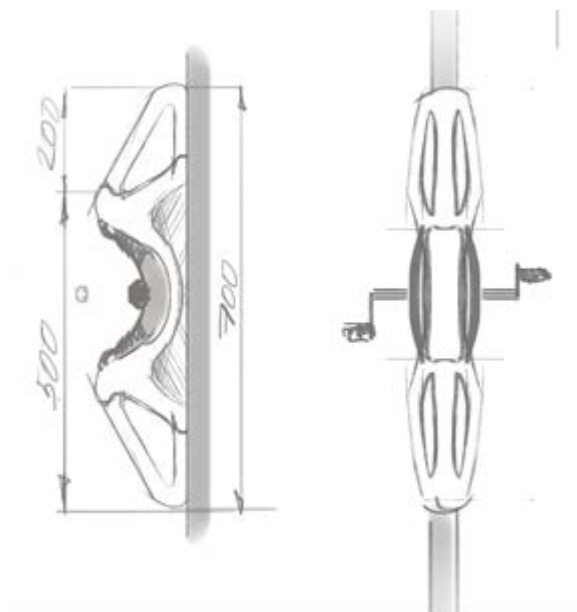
эскиз корпуса главного модуля «Lazar»
